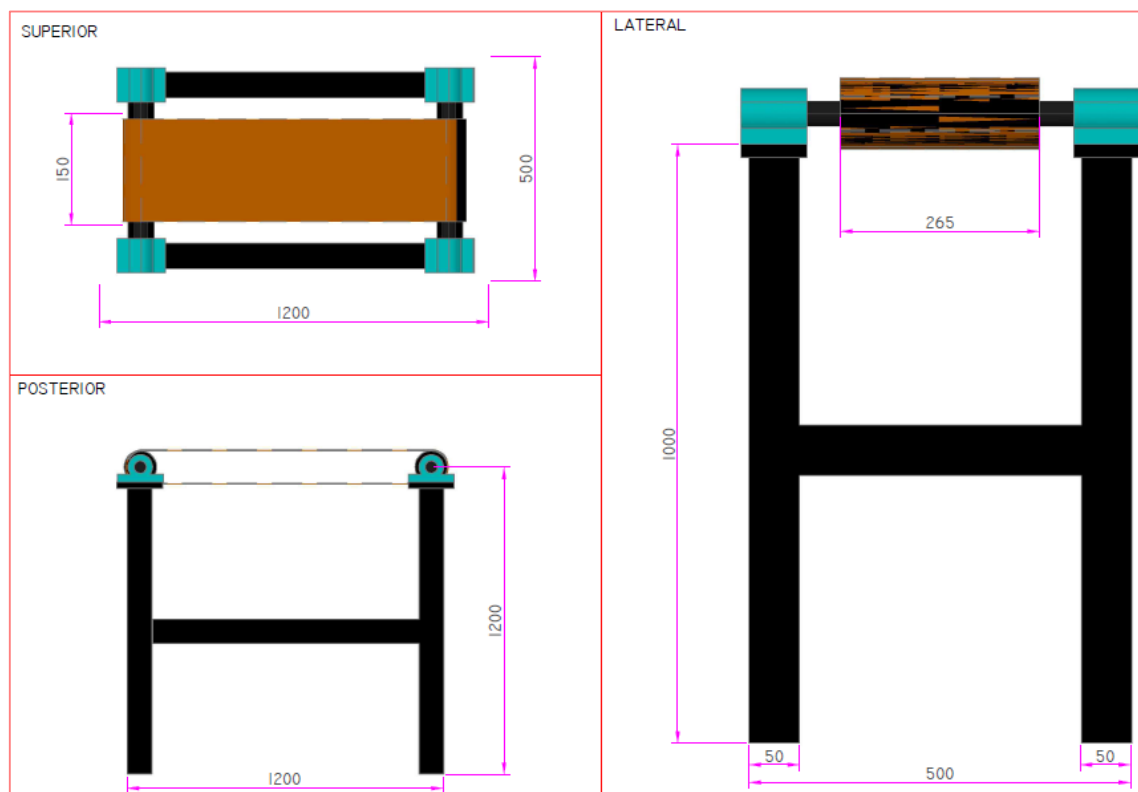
Plano esquemático de la mesa transportadora. Fuente: Autor.
